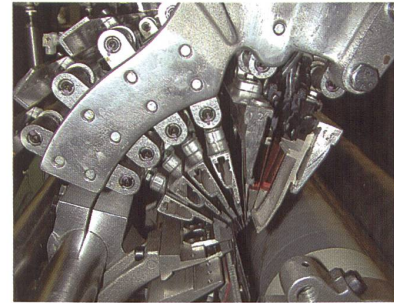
Wirkwerkzeuge der RSJ 5/1
